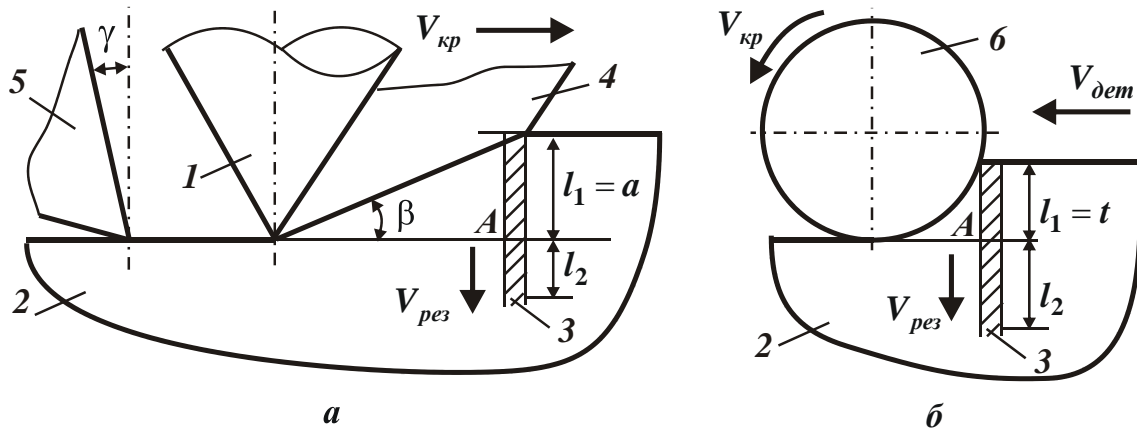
Расчетные схемы микрорезания отдельным зерном (резцом) (а) и шлифования (б): 1 – режущее зерно; 2 – обрабатываемый материал; 3 – адиабатический стержень; 4 – стружка; 5 – резец; 6 – шлифовальный круг.
